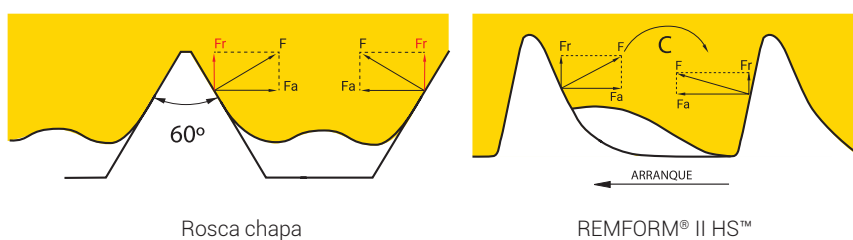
Descomposición de fuerzas en el flanco de carga y flanco de guía.
